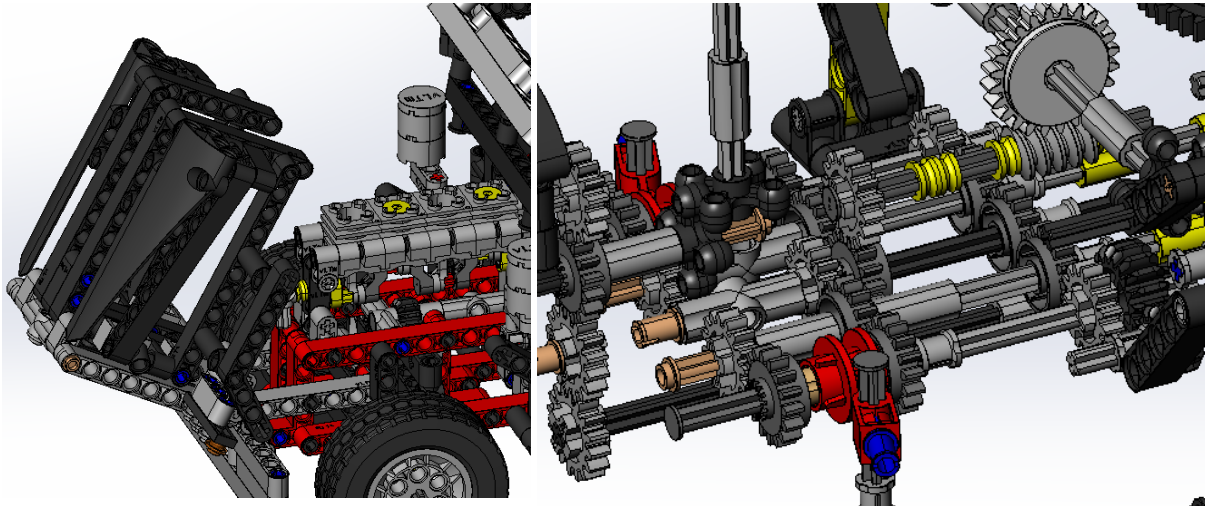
Sistema de engranajes (derecha) y mecanismo que permite ver el motor (izquierda).
